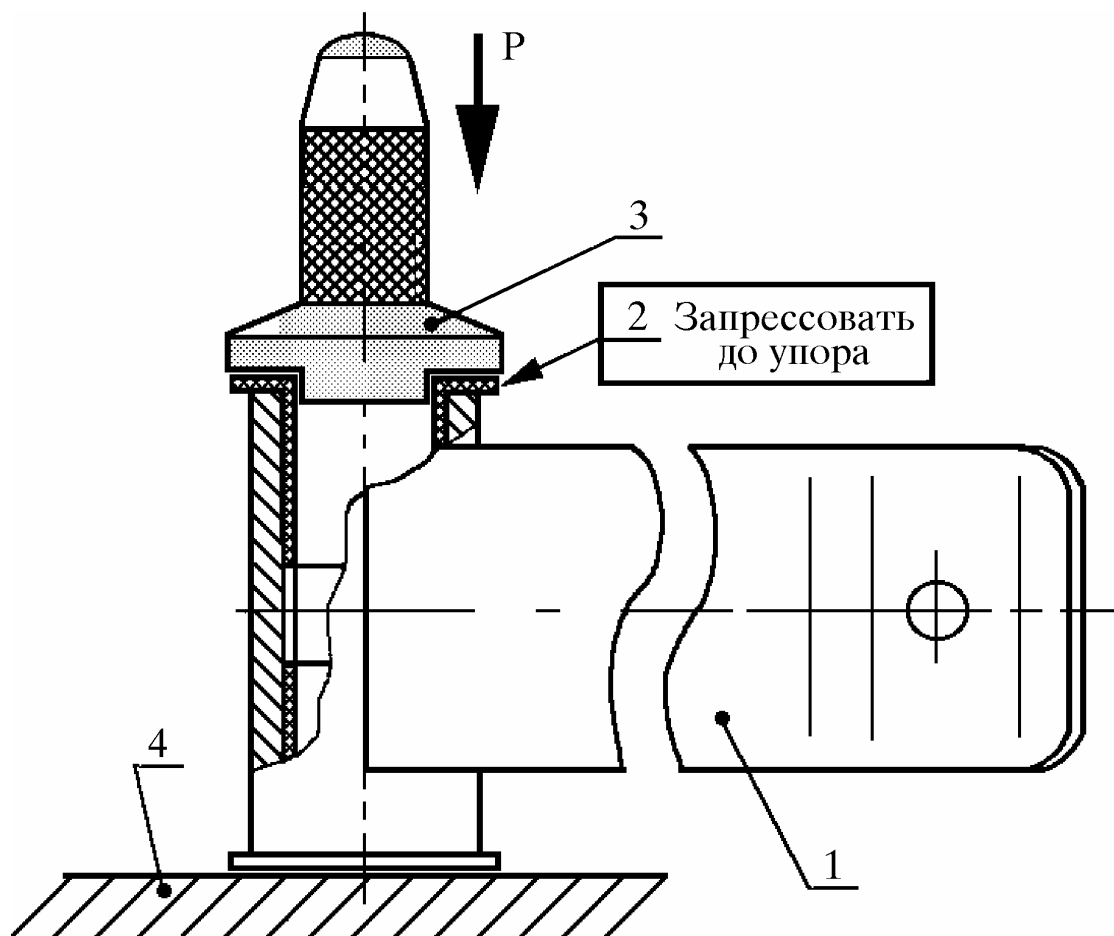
Запрессовка втулок в отверстие корпуса опоры рычагов механизма управления:
